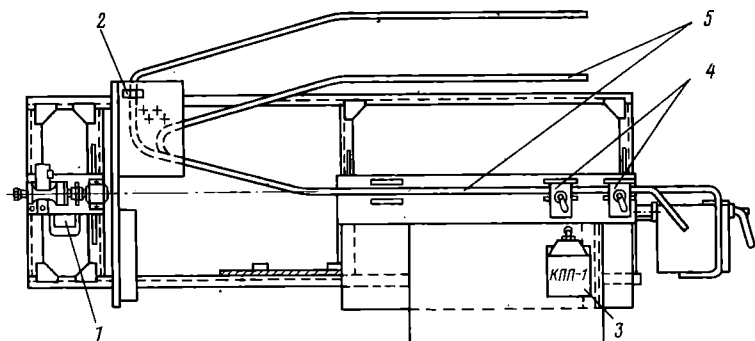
Кантователь для сварки трубных элементов:
